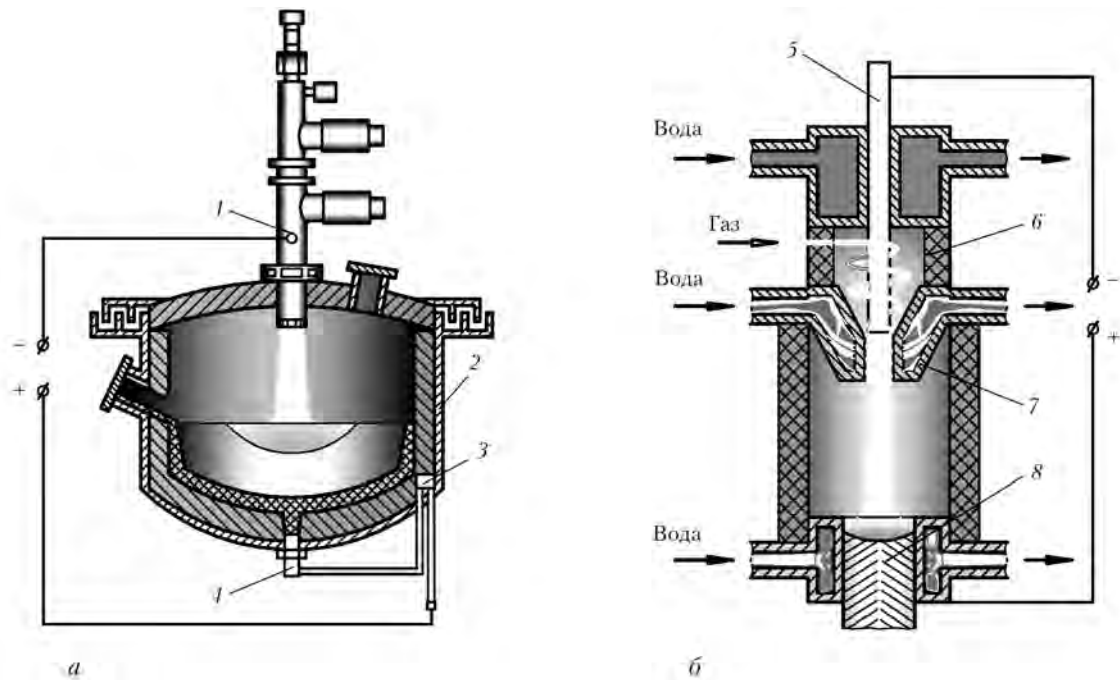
Схемы плазменно-дуговых печей для выплавки сталей и сплавов (а) и переплава заготовок (б): 1 — плазмотрон; 2 — камера печи; 3 — соленоид для перемешивания жидкого металла; 4 — подовый электрод-анод; 5 — электрод для переплава; 6 — камера; 7 — сопло плазмотрона; 8 — кристаллизатор
